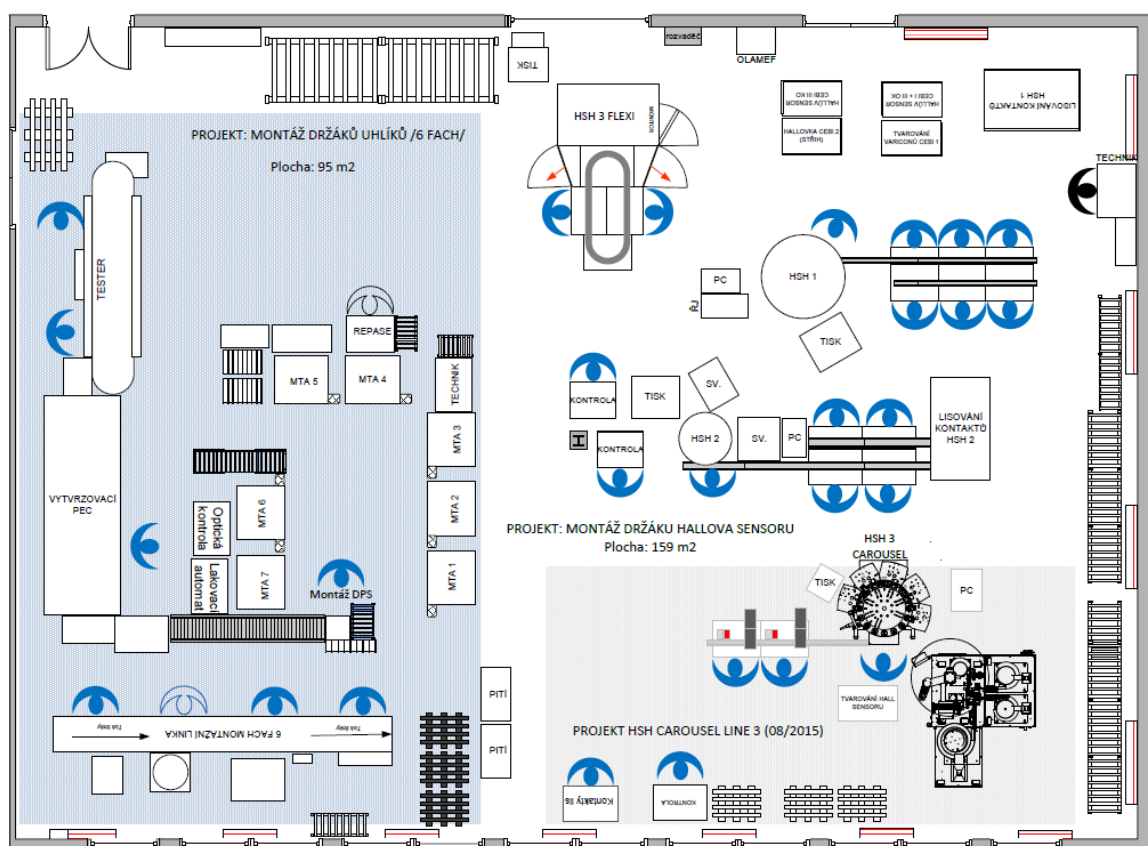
Původní layout výrobní haly (Vlastní zpracování)
